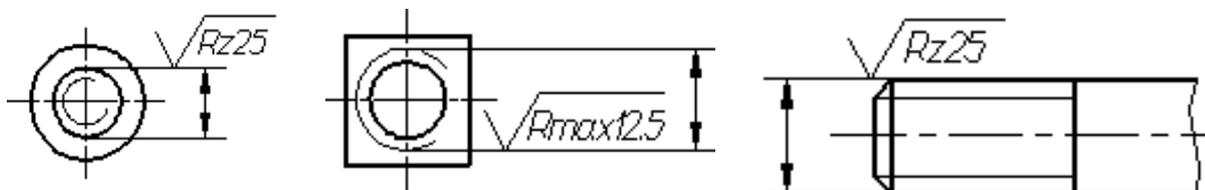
Обозначение шероховатости резьбы на выносной линии
